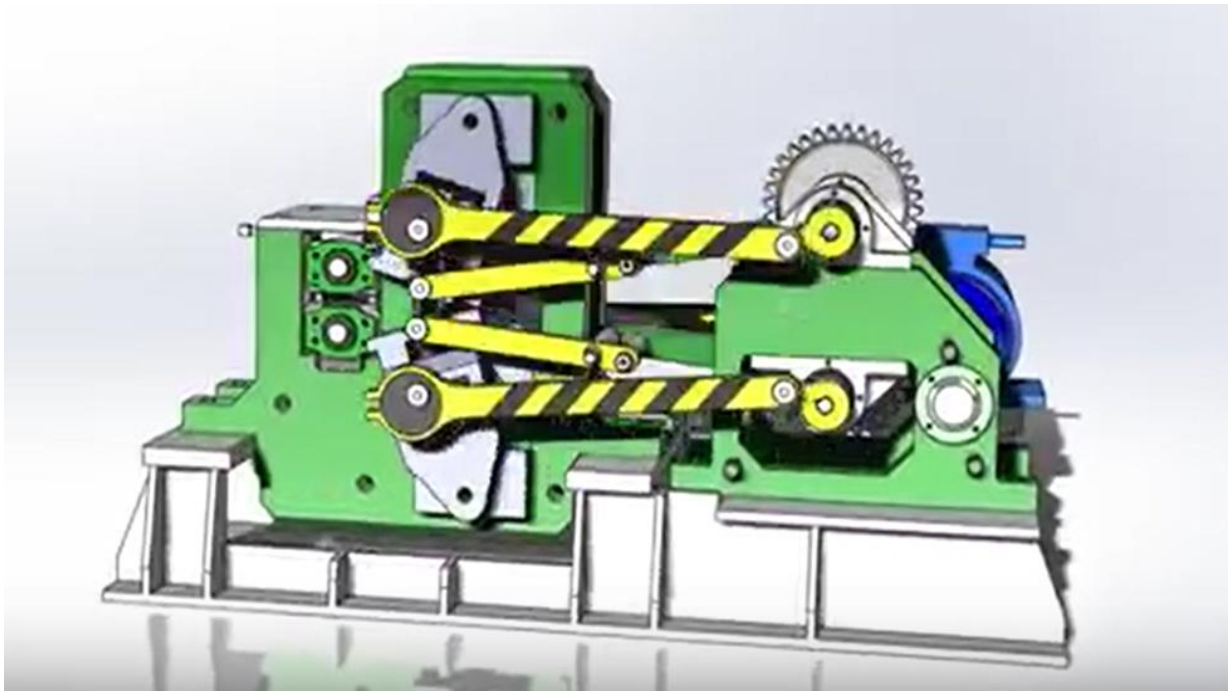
Общий вид маятникового стана с опорным профилированным валком
